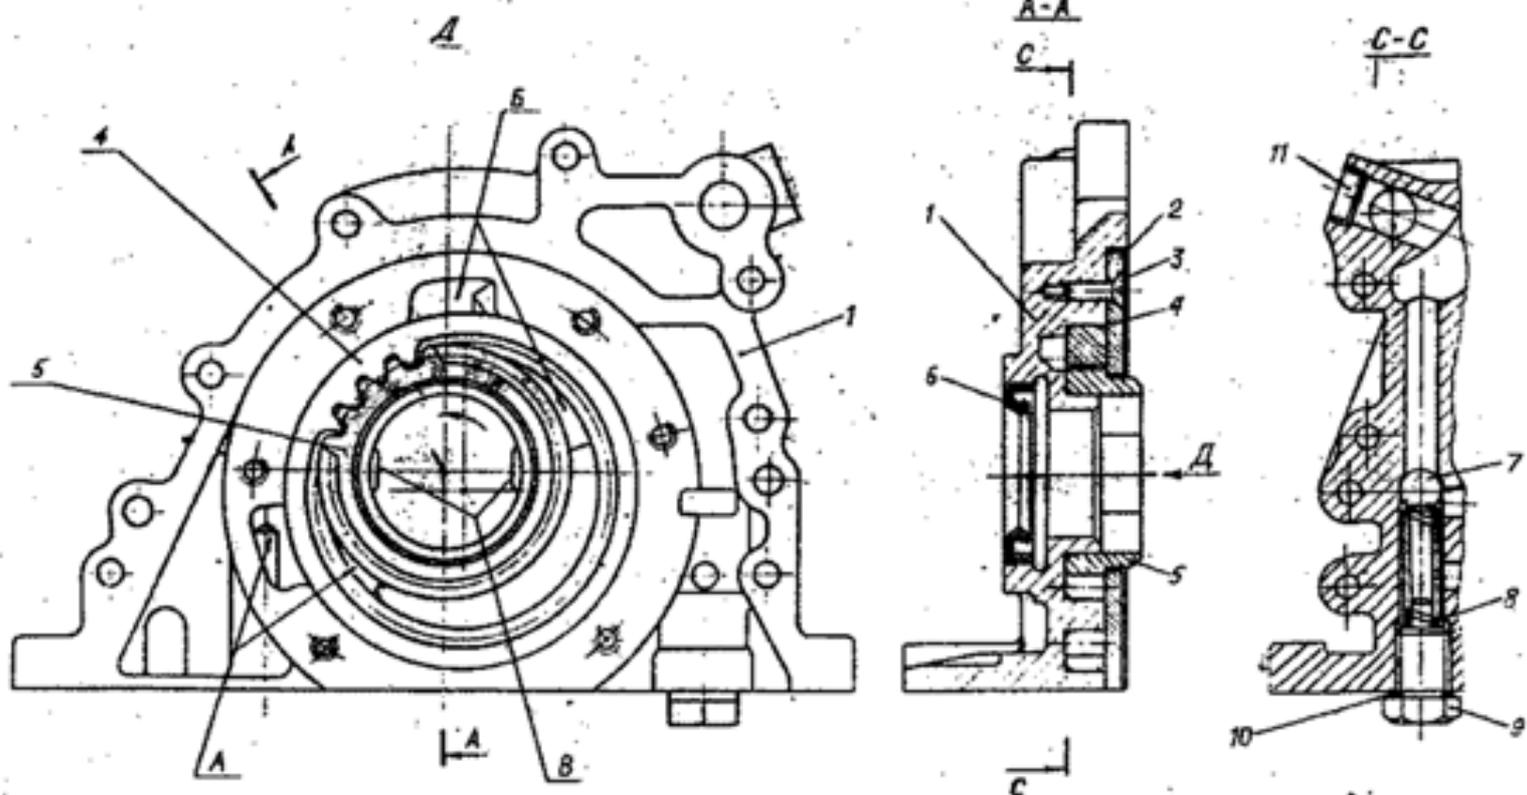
Масляный насос: 1 - корпус; 2 - крышка; 3 - винт; 4 - ведомая шестерня; 5 - ведущая шестерня; 6 - манжета; 7 - шариковый редукционный клапан; 8 - пружина редукционного клапана; 9 - пробка редукционного клапана; 10 - прокладка пробки; 11 - заглушка; В - выступ на ведомой шестерне; А - полость разрежения; Б - нагнетающая полость; вид Д - со снятой крышкой
